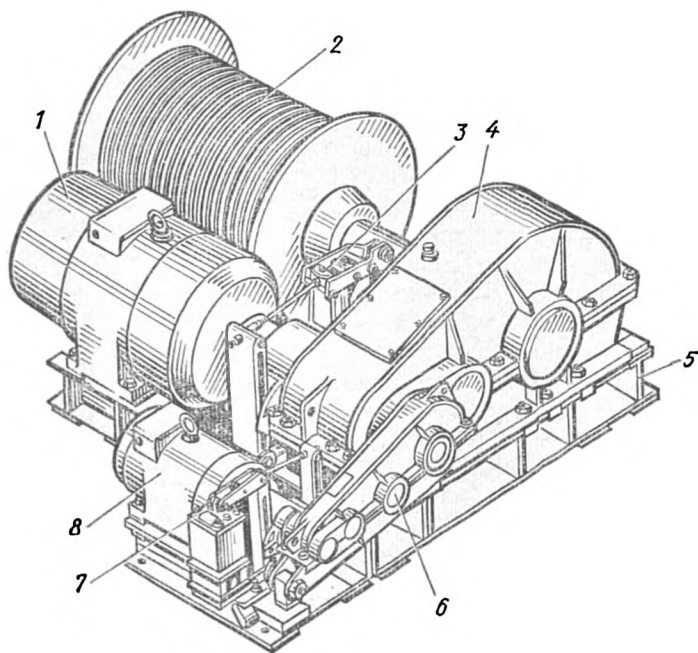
Грузовая лебедка основного подъема крана СКГ-40А:
